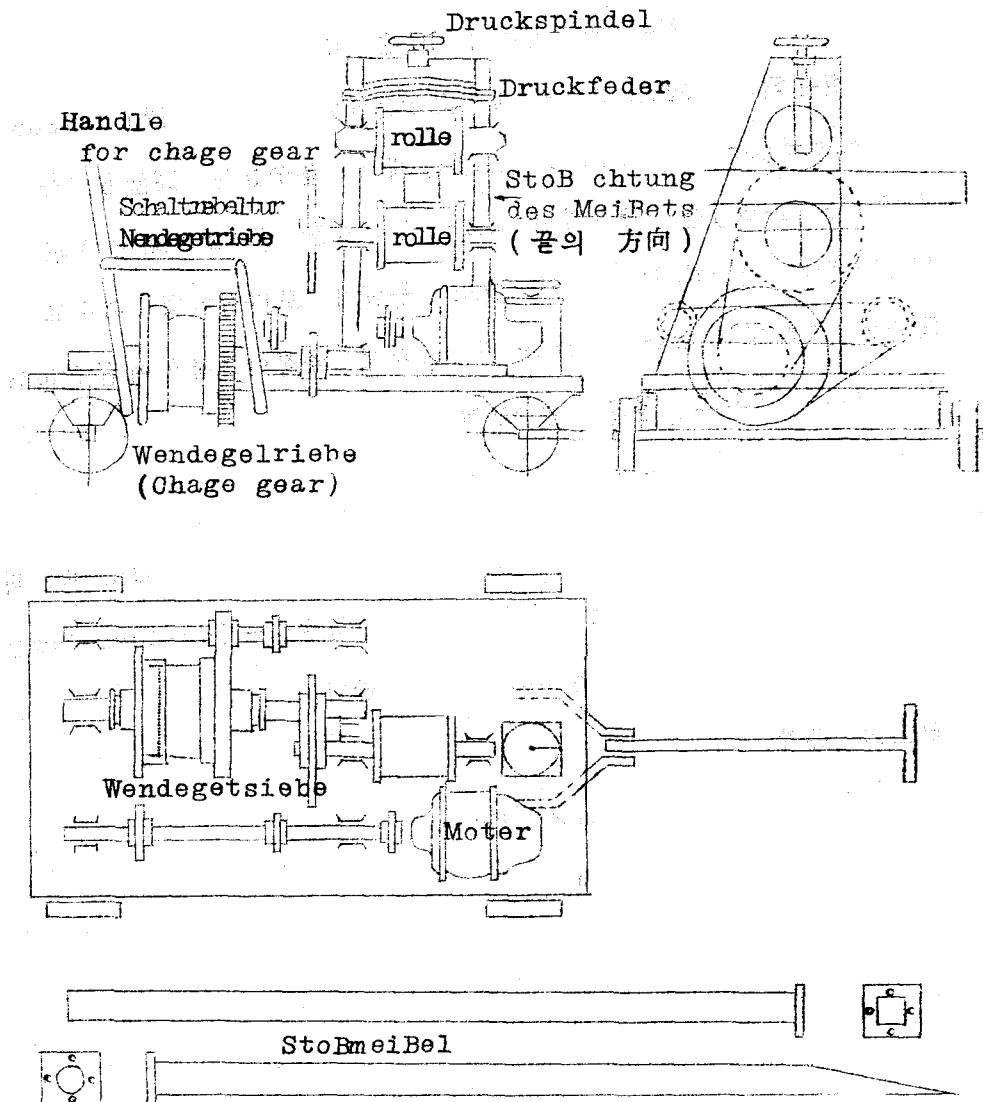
Wendegetriebe der Stoßmaschine zum Entfernen von Schlackenringen 切取장치의 gear
